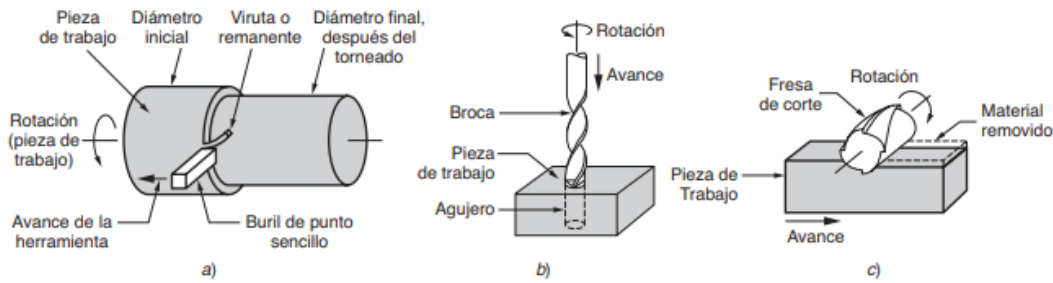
OPERACIONES COMUNES DE MAQUINADO: A) TORNEADO; B) TALADRADO; C) FRESADO [66].
